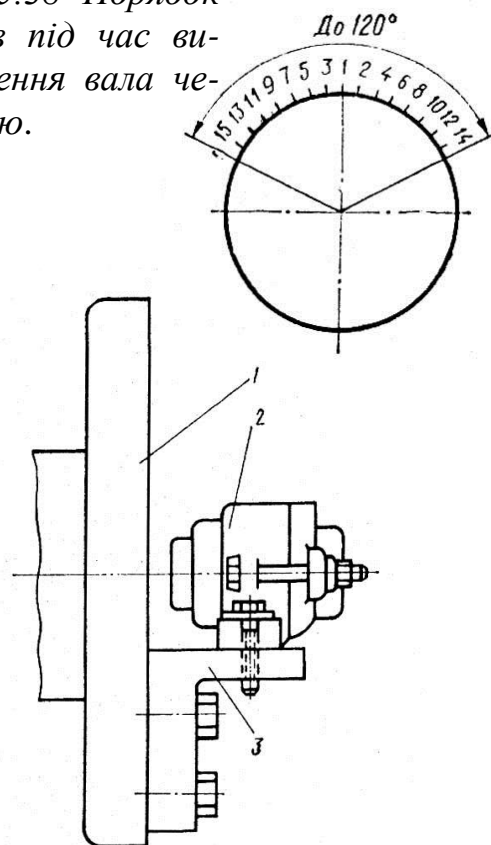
Закріплення корпусу підшипника для розточування на токарному верстаті:
